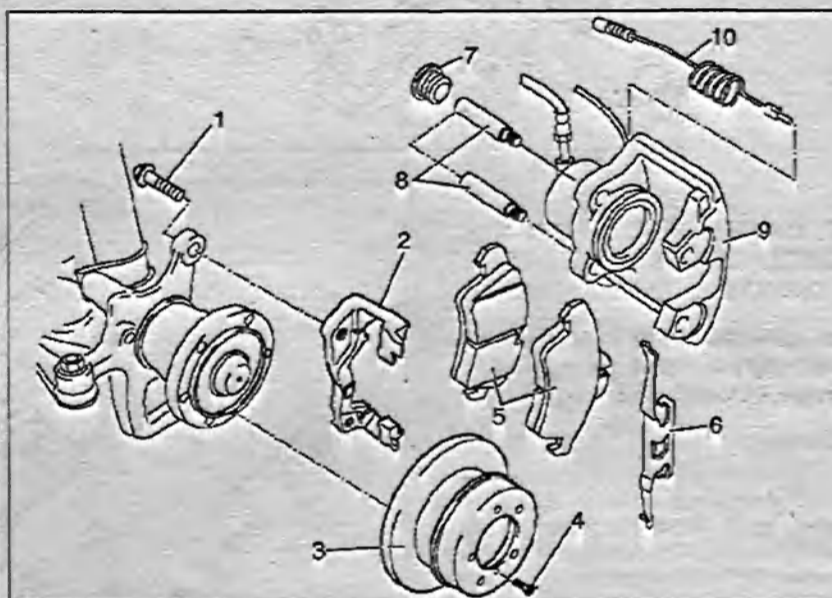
Тормозной диск переднего тормозного механизма: 1, 4 – Болты; 2 – Опора тормозного суппорта; 3 – Тормозной диск; 5 – Тормозные колодки; 6 – Пружинный фиксатор; 7 – Пробка; 8 – Направляющие пальцы; 9 – Тормозной суппорт; 10 – Индикатор износа тормозной колодки.
